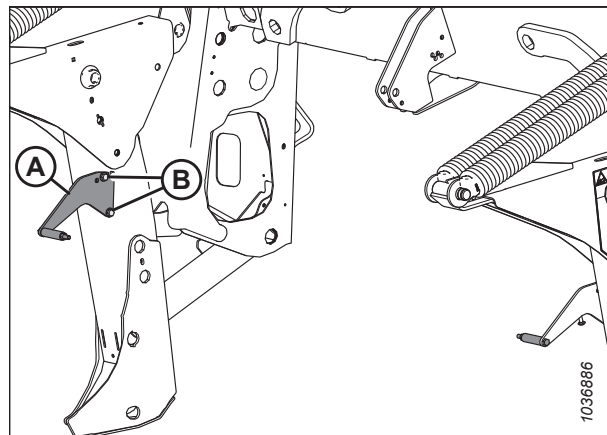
Кронштейн формовочного щитка — серия R2
